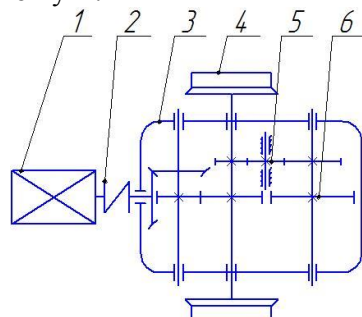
Модернизируемый приводной редуктор шахтного электровоза
